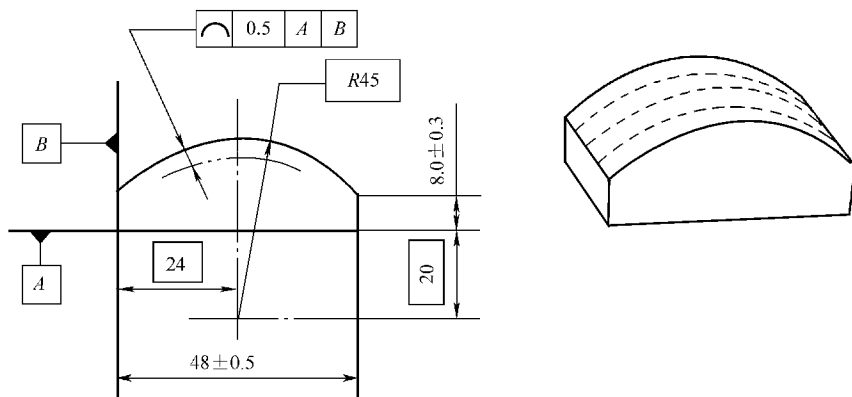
一个零件的线轮廓度几何公差定义
